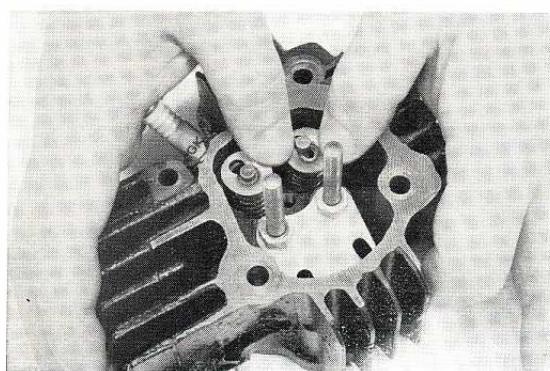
DEMONTAGE DE LA SOUPAPE.
